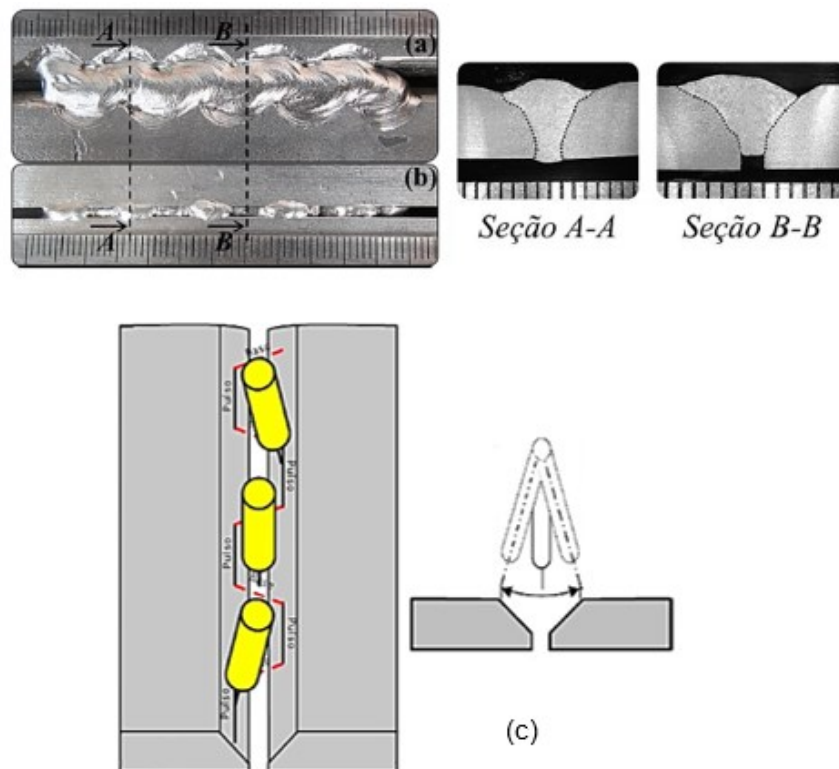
Cordões de solda executados na posição 5G. Fonte: [23]
